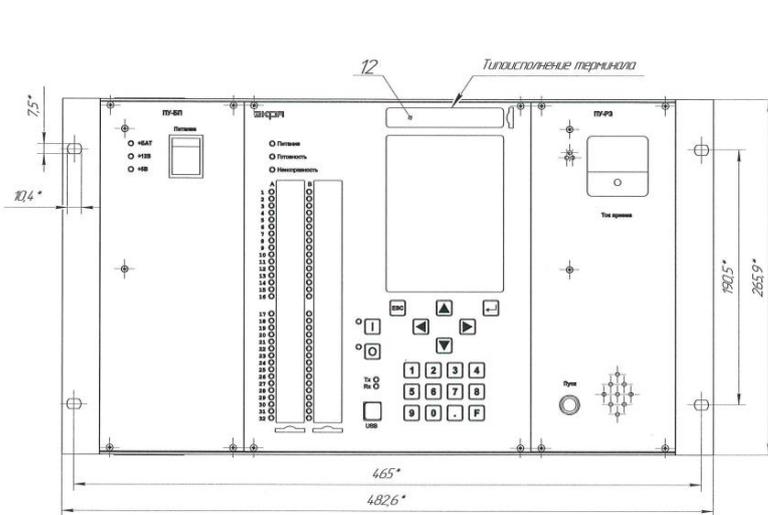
Габаритные и установочные размеры ЭКРА 253 0201 (вид спереди)
